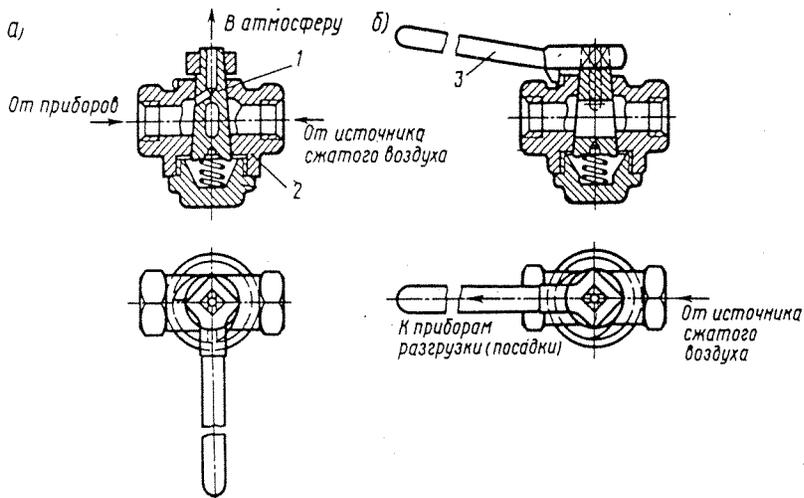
Кран управления разгрузкой и посадкой 1-4 (ОСТ 24.290.16-86): а — транспортное положение; б — положение разгрузки; 1 — клапан; 2 — корпус; 3 — ручка
